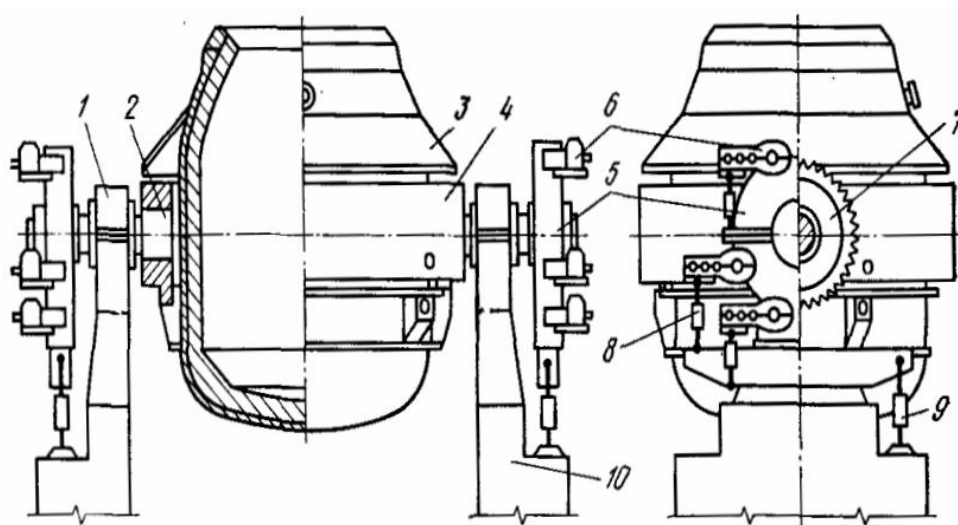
Кислородный конвертер с навесным многодвигательным приводом: 1 — опорный подшипник; 2 — цапфа; 3 — защитный кожух; 4 — опорное кольцо; 5 — корпус ведомого колеса; 6 — навесной электродвигатель с редуктором; 7 — ведомое зубчатое колесо; 8 — демпфер навесного электродвигателя; 9 — демпфер корпуса ведомого колеса; 10 — опорная станина
